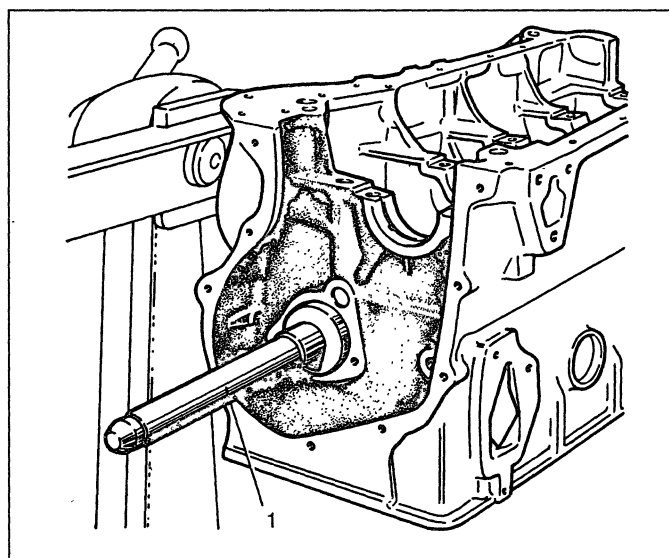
Снятие и установка втулок валика привода масляного насоса и распределителя зажигания: 1 – оправка А.60333/1/2
